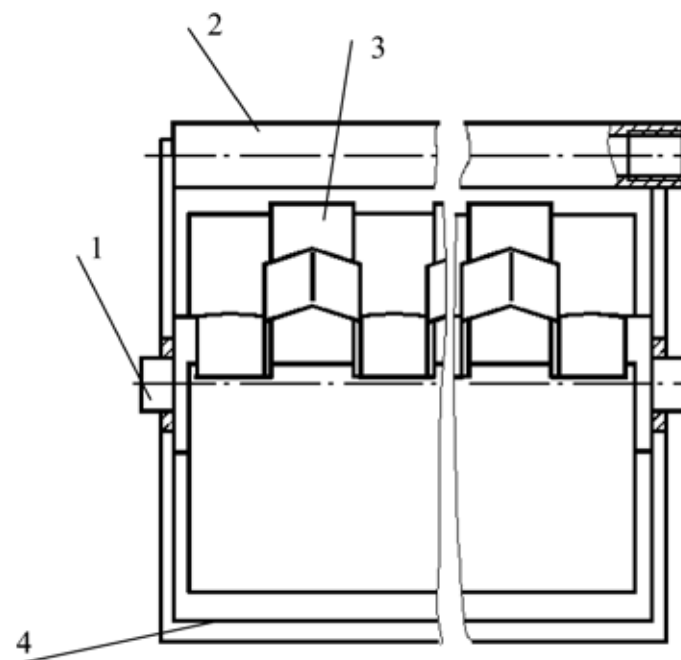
Схема размещения приспособления для очистки шламоборных цилиндрических магнитных дисков (вид с боку):
